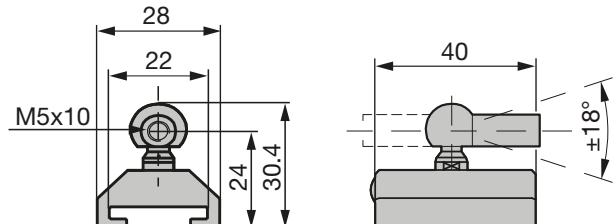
Medidas de montaje del sensor de posición BTL5-F-2814-1S
